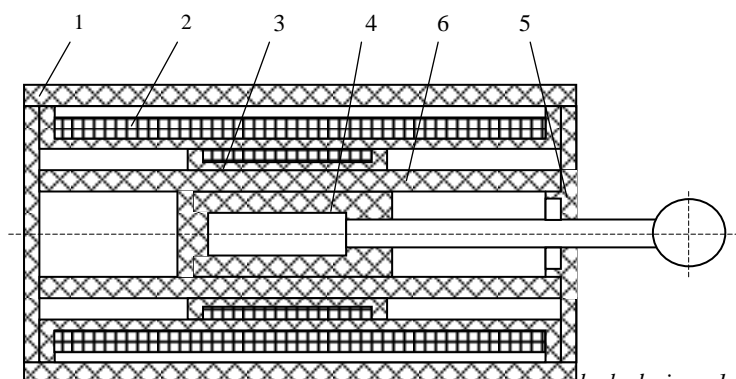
Конструкция измерительного блока. 1 - корпус; 2 - соленоид; 3 - измерительная катушка; 4 - досылатель; 5 - ограничитель; 6 - трубка
